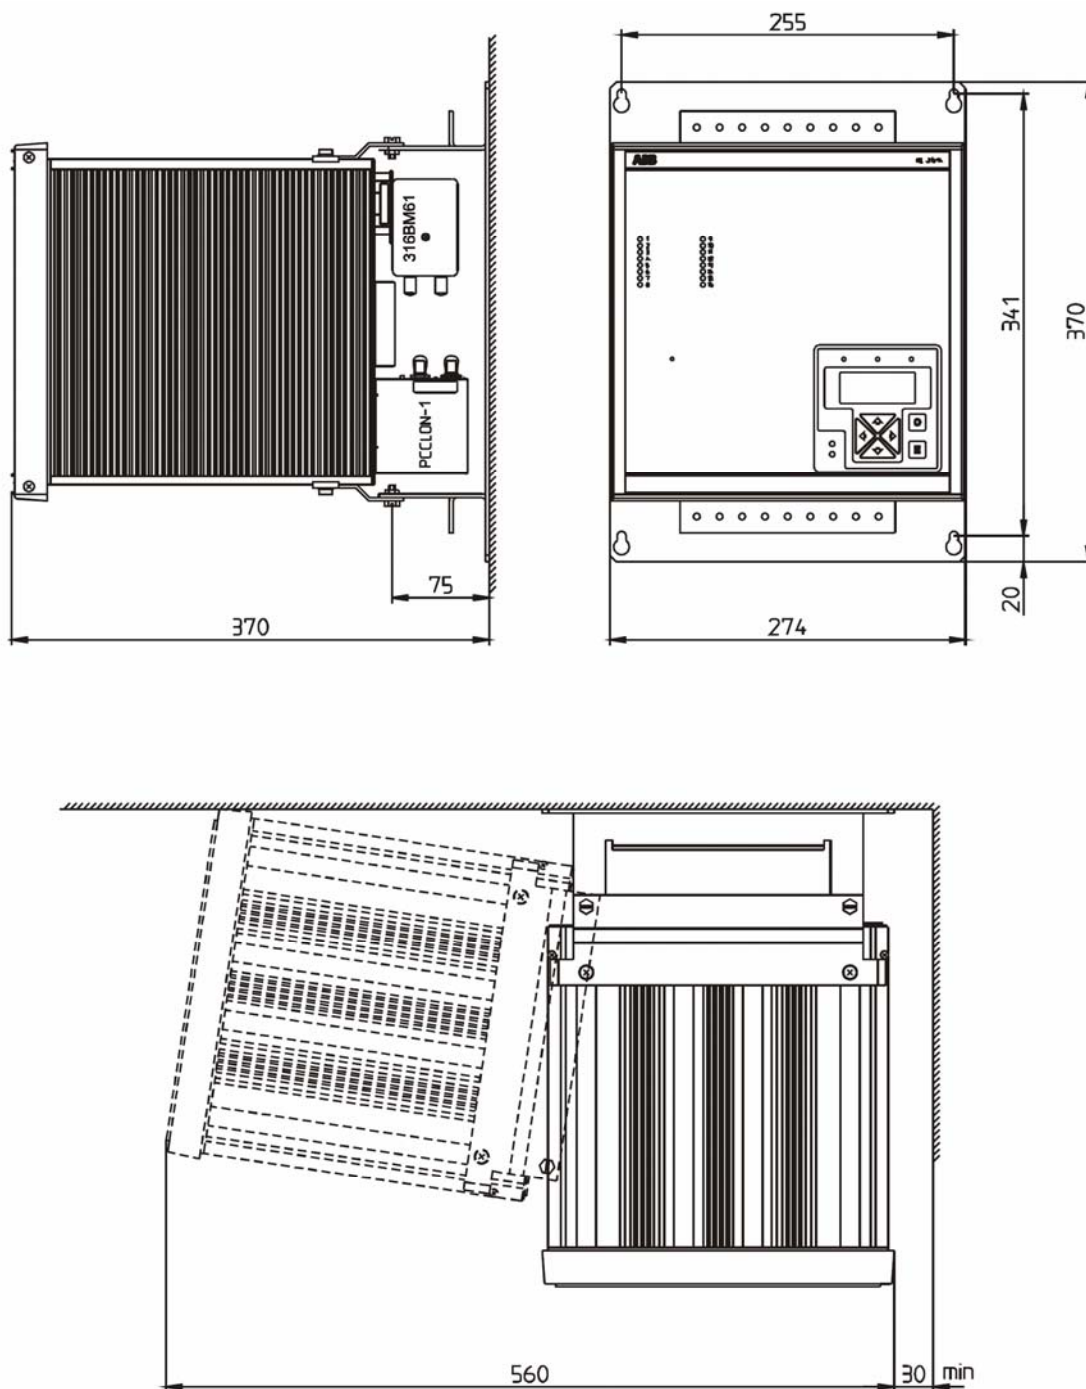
Навесной монтаж, корпус может поворачиваться влево, заднее присоединение, корпус размером N2
